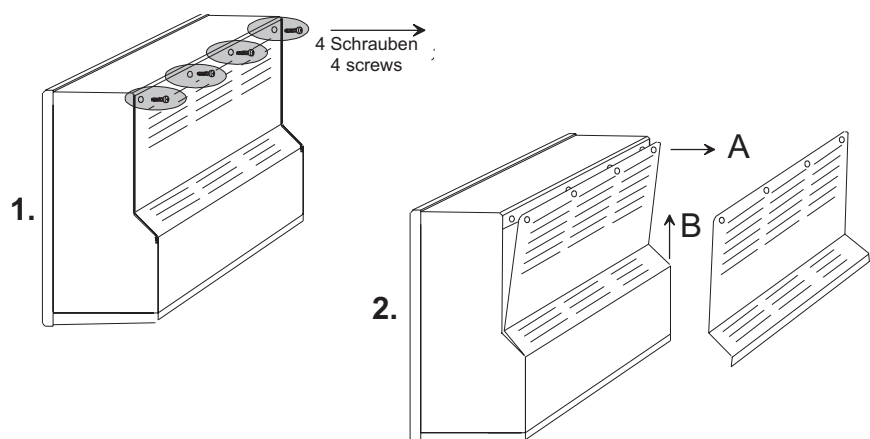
Entfernen des rückseitigen Abdeckblechs
